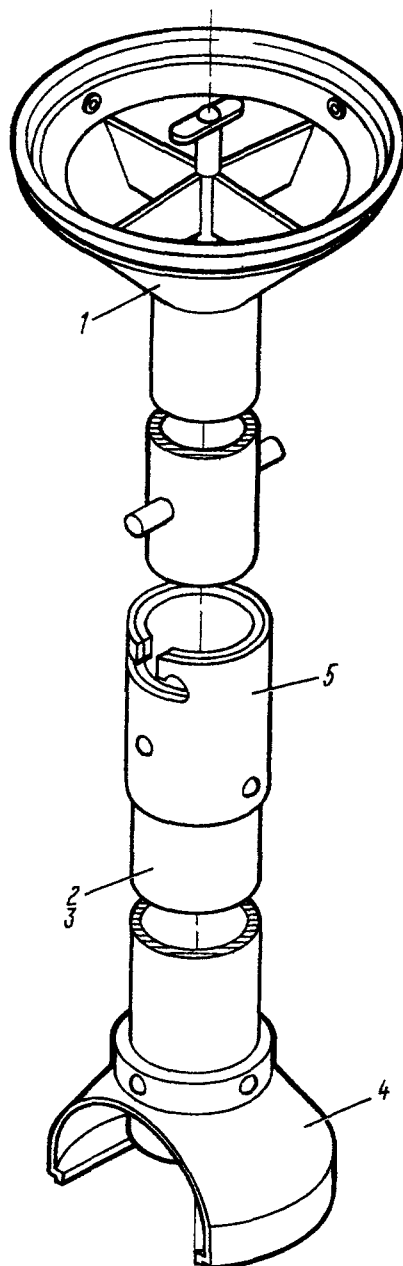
ВОРОНКА ДЛЯ СЛИВА КОНДЕНСАТА ИЗ БАКОВ
